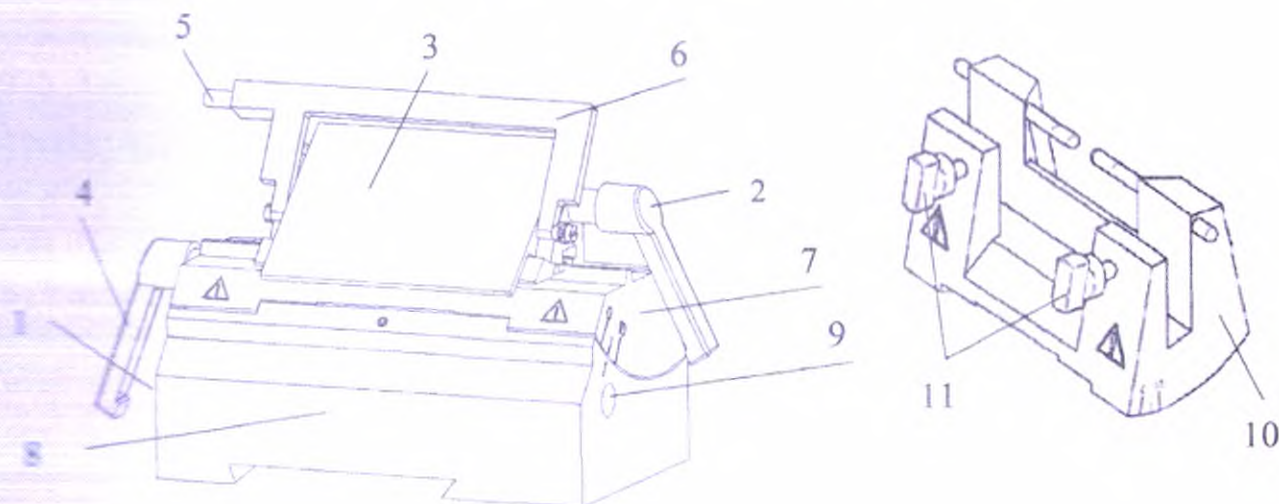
Установка держателя стального ножа, держателя лезвия и его основания
